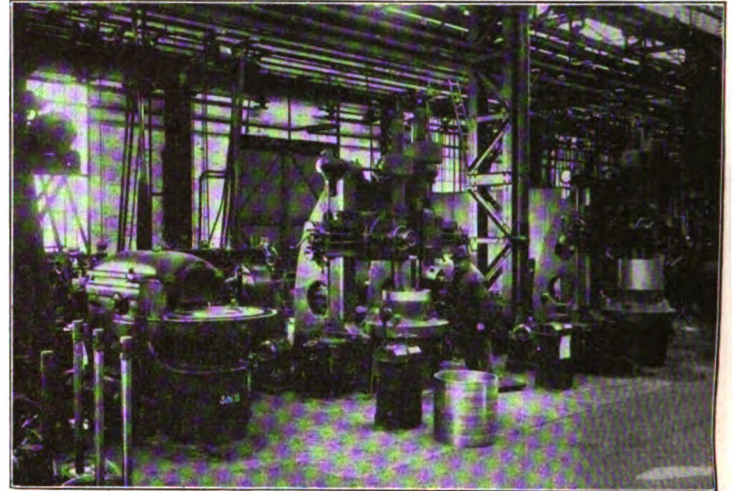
Fertigung der Kolbenringe auf drei Arbeitsmaschinen.
